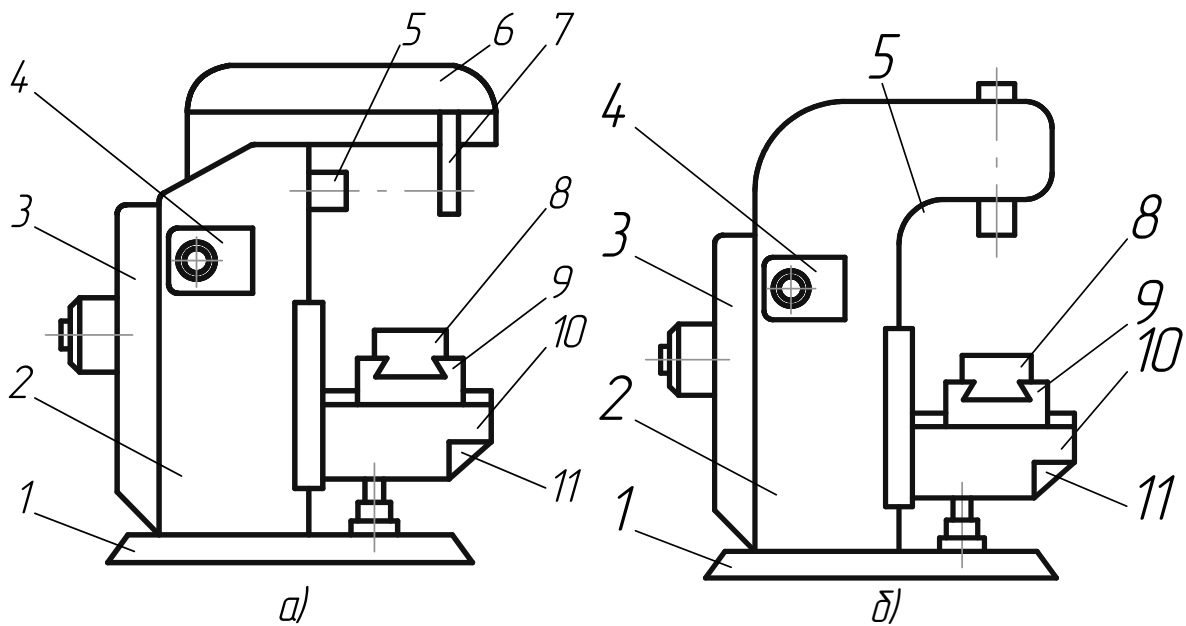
Схеми горизонтально-фрезерного (а) та вертикально-фрезерного (б) верстатів
